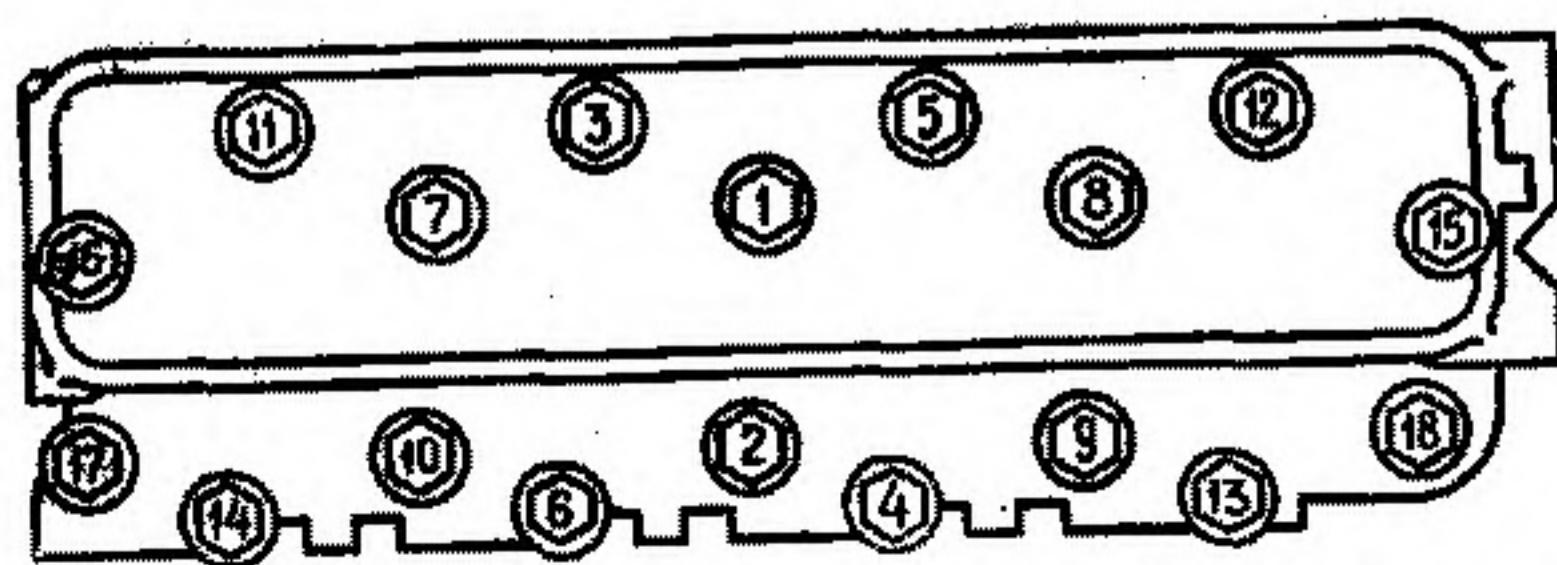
Последовательность затяжки гаек шпилек крепления головок блока цилиндров
